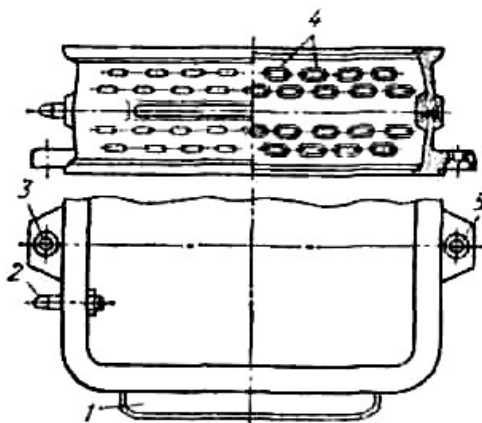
Опока для формовочного автомата: 1 — направляющая планка; 2 — штырь для кантовки; 3 — центрирующая втулка; 4 — вентиляционные отверстия; 5 — направляющая втулка
